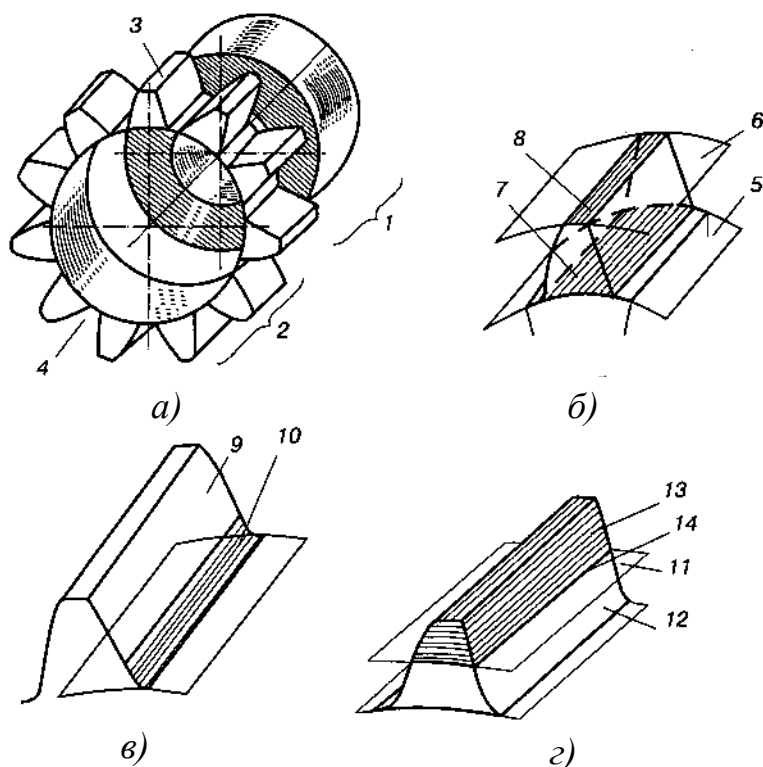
Основні елементи циліндричного зубчатого колеса
